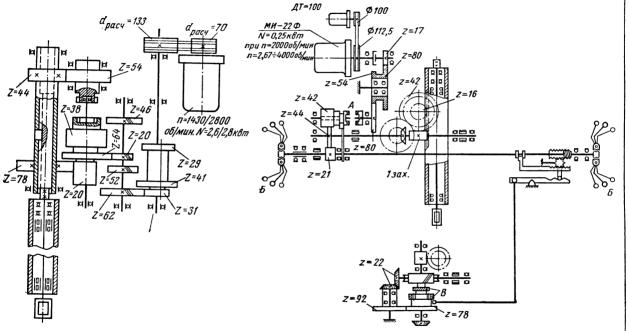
Кинематическая схема привода главного Рис. 13. Кинематическая схема подач пиноли шпинделя станка модели ЛР-87
